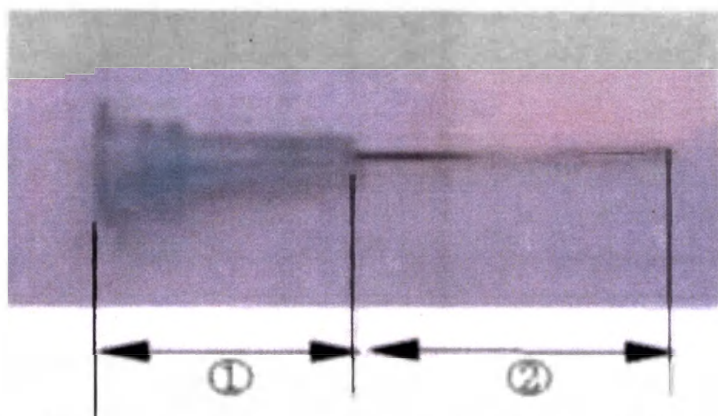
Схема общего вида 1- длина головки иглы, 2- длина рабочей части иглы
